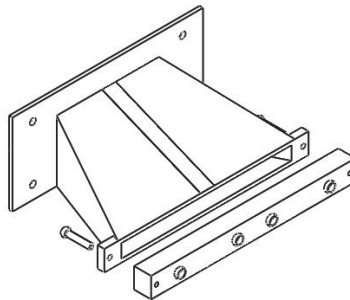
Ensamble boquilla de cabezal con placa de inyección
